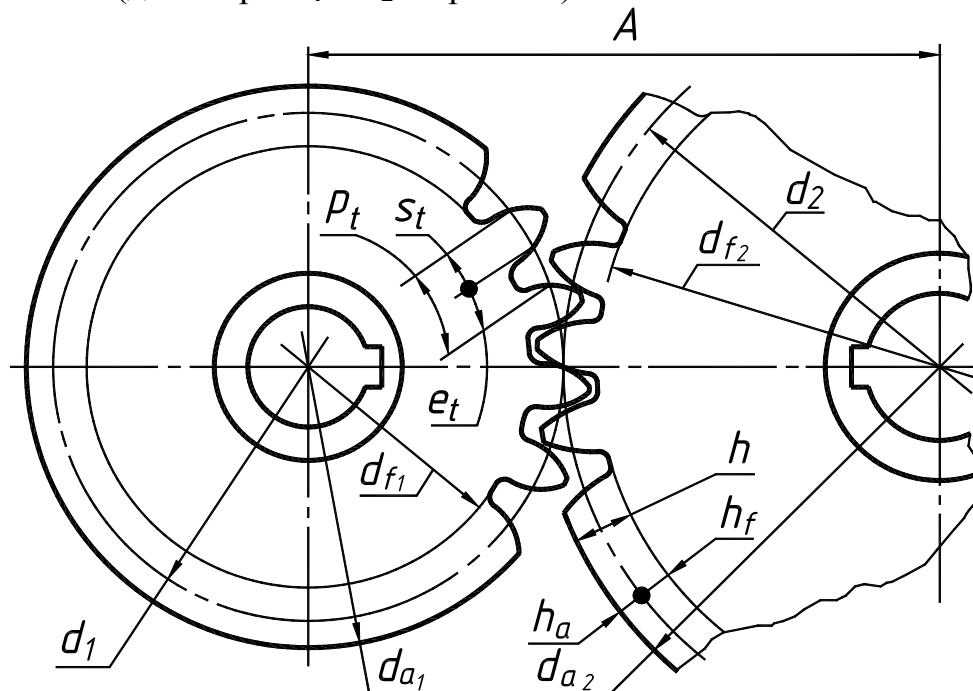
Геометрические параметры цилиндрической зубчатой передачи
